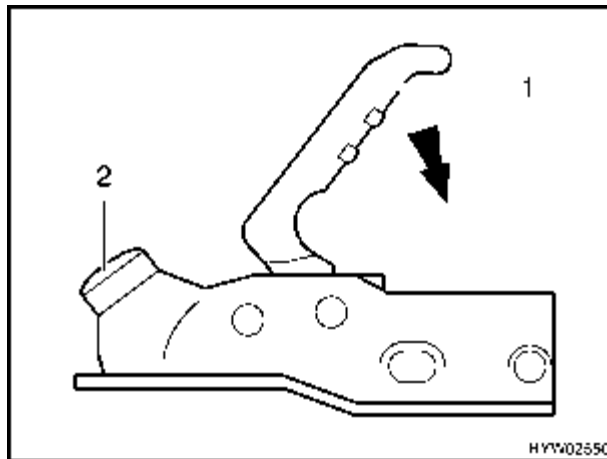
Acoplamiento de remolque AL-KO AK 300/160
